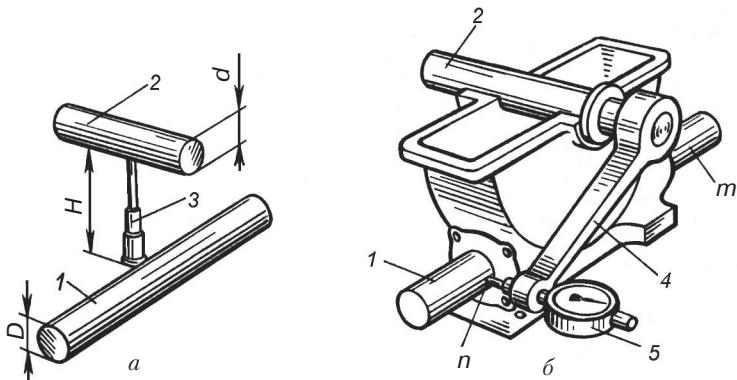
Контроль розташування осей отворів у корпусі редуктора:
